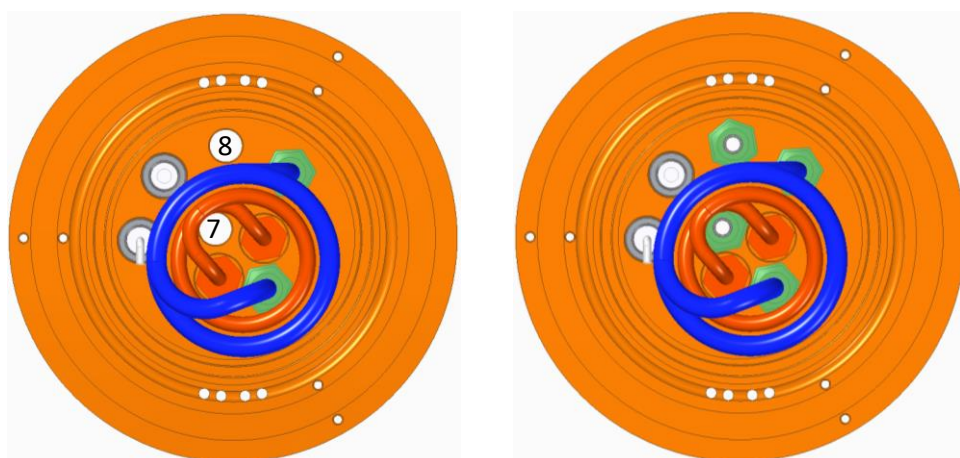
Draufsicht des Boilerbodens zur Montage des Druck- und Steigrohres in den Bohrungen 7 und 8
